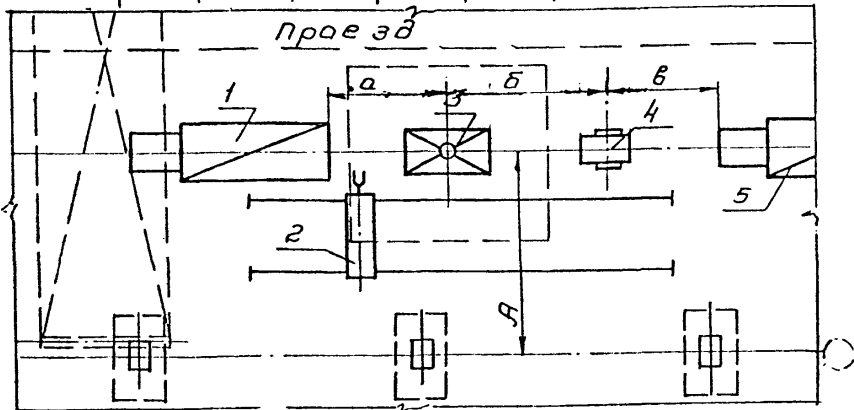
Схема расположения штамповочных линий на базе ПШЛ с напольным манипулятором:
